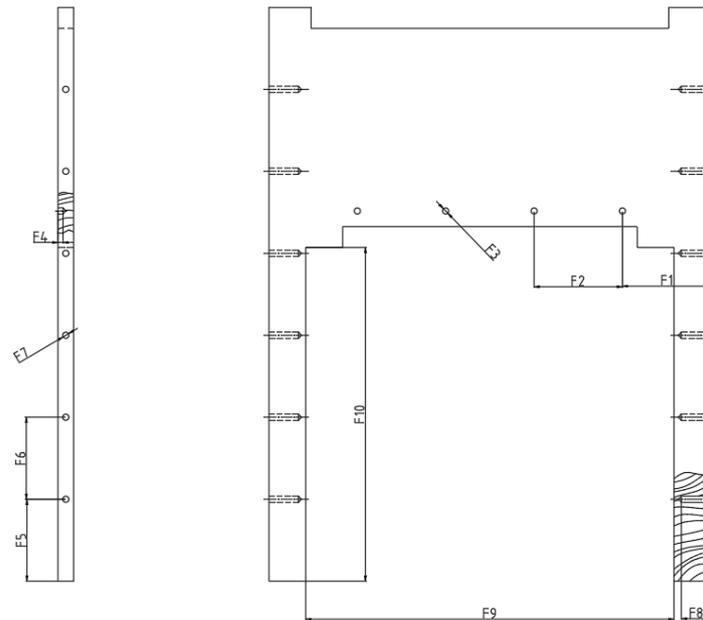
Plano Dimensionado Previo del Lateral Baúl 1.1.3
